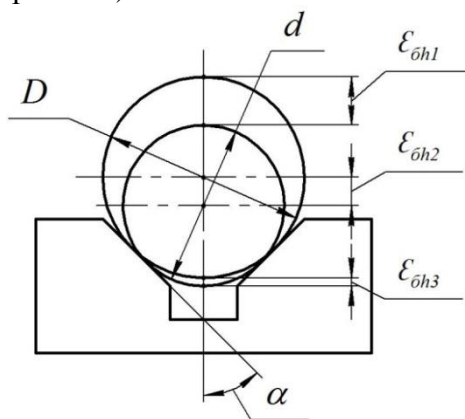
Базування деталі по циліндричній поверхні на призмі
